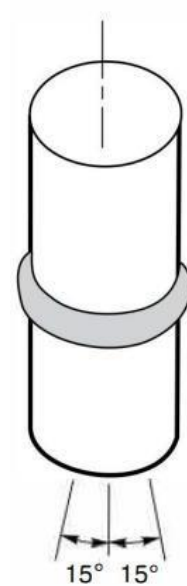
6 Flat Welding Test Position 1G⁹
